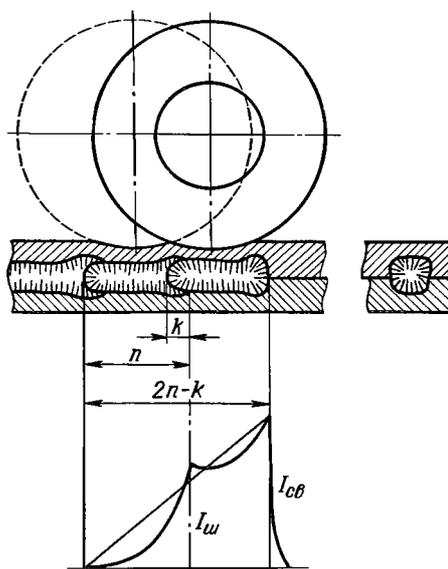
Структура шовно-сварных соединений и схема шунтирования сварочного тока
